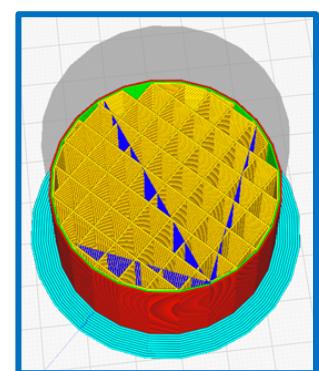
Estructura interna d'un cilindre (Font: Pròpia)
